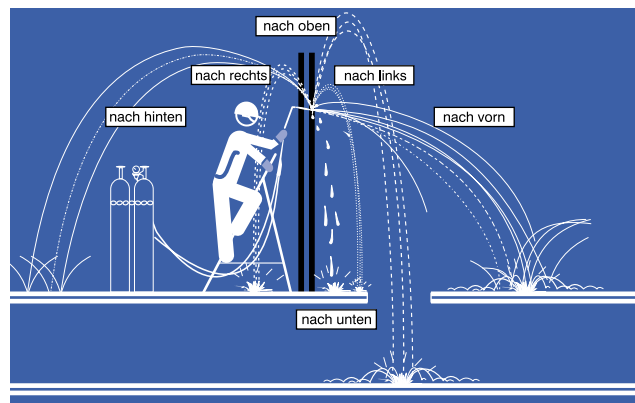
Ausbreitungsverhalten heißer Partikel bei schweißtechnischen Arbeiten
